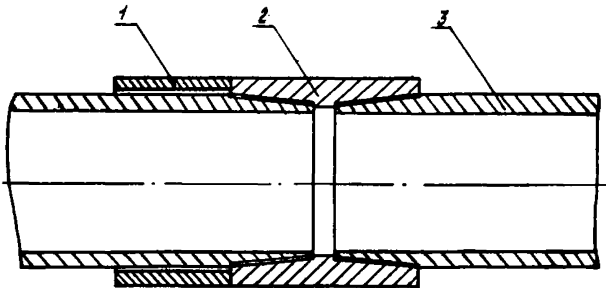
Установка образца снаружи насосно-компрессорных труб:
